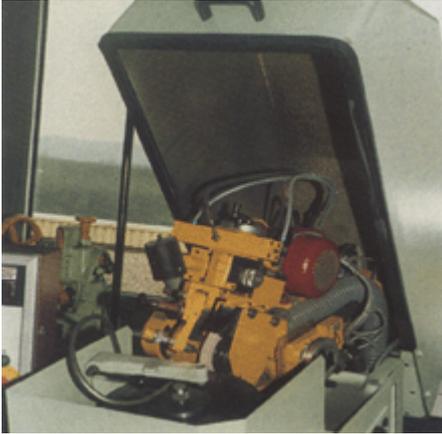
Sägeblatt-Schleifmaschine. Die Schalldämmhaube ist in die Maschinenkonstruktion integriert
